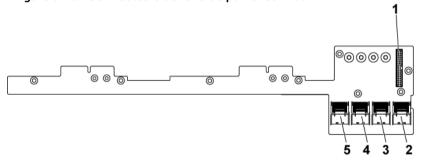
Vue du haut de la carte d'extension de disques durs 2,5 pouces
